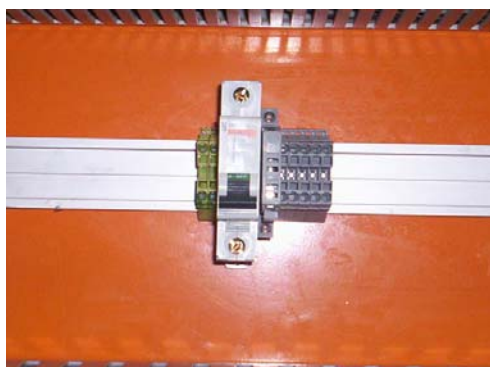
Montaje de Disyuntor, portafusible y borneras en Estación Elevadora.
